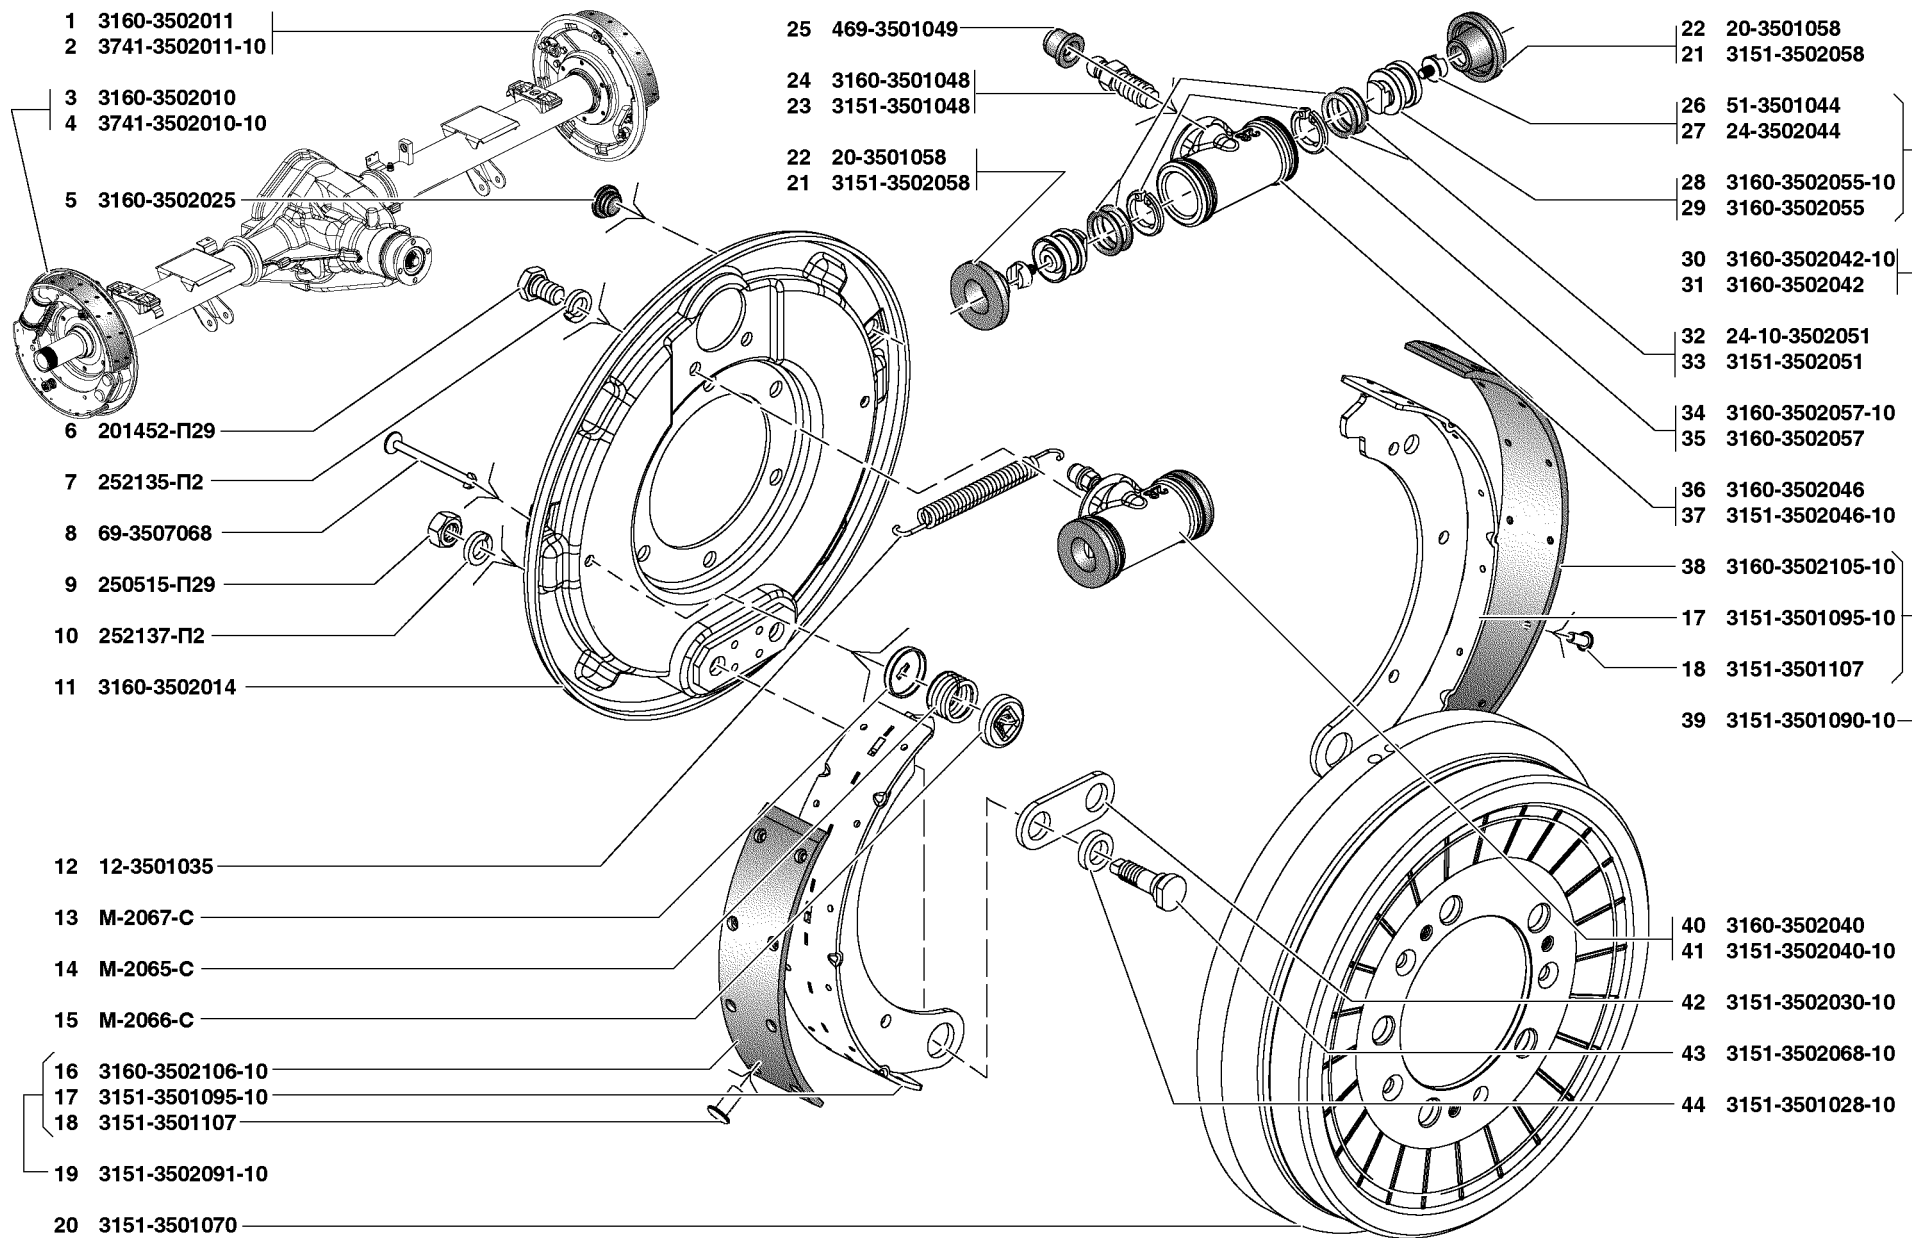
Тормоза рабочие задние и тормозные барабаны (3502)
